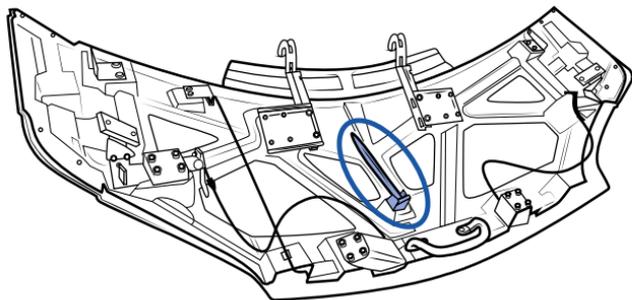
Mécanisme de la pompe hydraulique de la cabine
